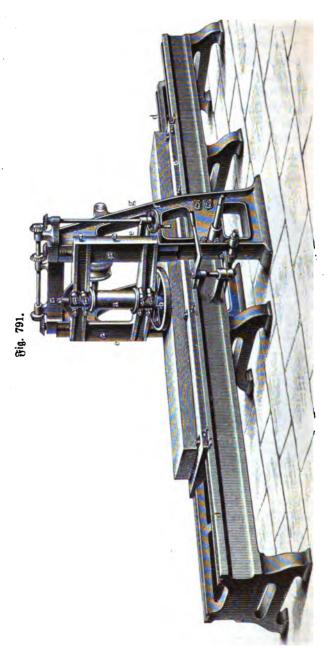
Die Messer ragen aus ber unteren Fläche ber auf ber sentrechten Spinbel a besestigten Scheibe b hervor, die durch einen auf a gessührten halbgeschränkten Riemen schnell umgedreht wird, während das zu hobelnde Holz auf der Tischplatte c durch geeignete Spannvorrichtungen besestigt ist. Wenn diese in den prismatischen Führungen des Bettes a geleitete Tischplatte in der von den Metallhobelmaschinen her bekannten, in der Figur nicht näher erläuterten Art langsam verschoben wird, so wird durch die Messer oder stichelförmigen Schneiden der Scheibe b die obere Fläche des Holzes in der schon oben besprochenen Weise abgerichtet. Die Messerwelle sindet hierbei ihre Lager in einem Rahmen e, der an den senkrechten Führungsbahnen des Gestelles g vermittelst der beiderseits angebrachten Schraubenspindeln durch Umdrehung des Handrades f sehr genau verstellt werden kann, so daß man hierdurch nicht nur die Stärke des abzunehmenden Spanes in der Hand hat, sondern auch den jeweiligen Dicken verschiedener Hölzer entsprechend die Stellung der Messerschiede bestimmen kann.
